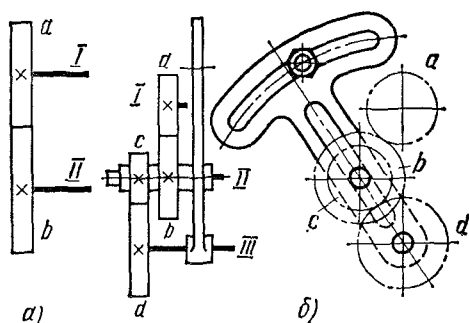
Множительные механизмы со сменными зубчатыми колесами
